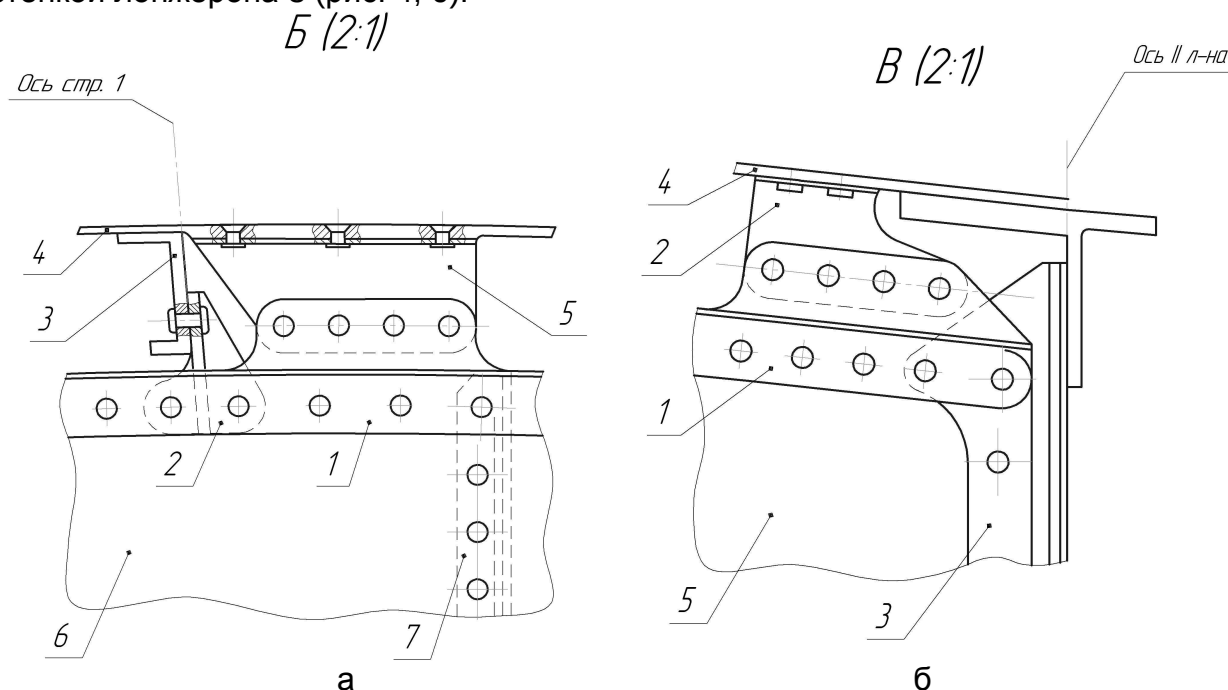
Фрагмент чертежа типовых соединений пояса с элементами нервюры, продольного набора крыла и обшивкой:
